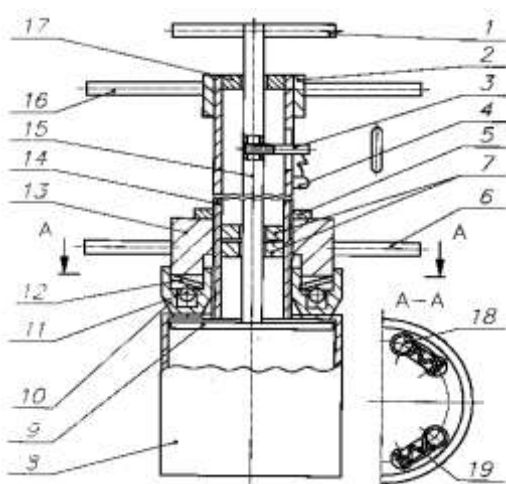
Устройство для вырезания отбора проб почвы: 1 — ручка выталкивателя; 2 — муфта; 3 — поводок; 4 — выключатель концевой; 5 — контргайка (ГОСТ 8961-75); 6 — упор нижний; 7 — втулка направляющая; 8 — нож цилиндрический; 9 — выталкиватель; 10 — корпус; 11 — шарик; 12 — пружина дисковая; 13 — муфта; 14 — труба (3/4"); 15 — труба (8–10); 16 — упор верхний; 17 — втулка направляющая; 18 — шарик; 19 — пружина
